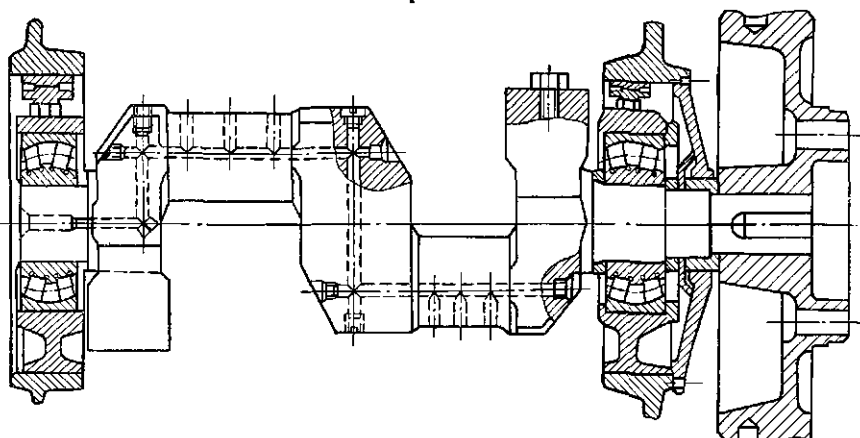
Конструкция двухопорного коленчатого вала многорядного компрессора
